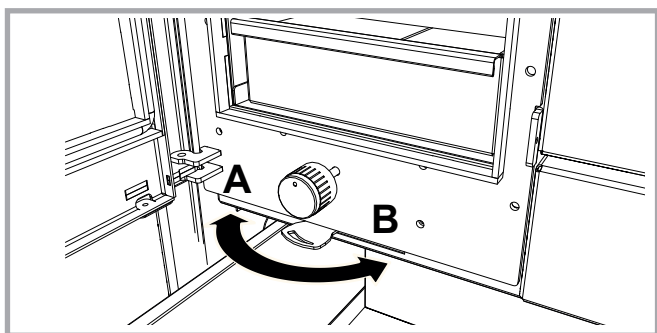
Einstellung der Frischlufztzufuhr-Regulierung. Wenn sich der Hebel auf der Position "A" befindet, ist die Luftzufuhr offen. Auf der Position "B" ist die Luftzufuhr geschlossen.
